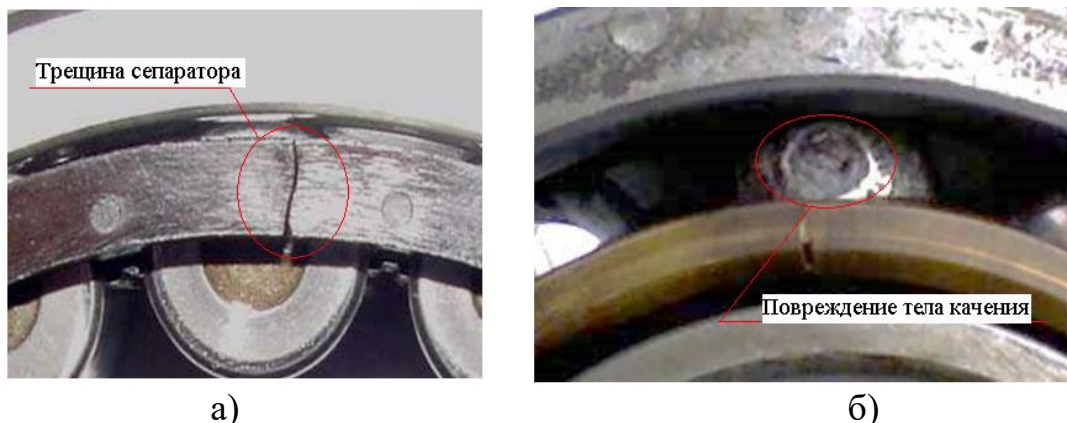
Осмотр подшипника: а) трещина сепаратора; б) повреждение тела качения
